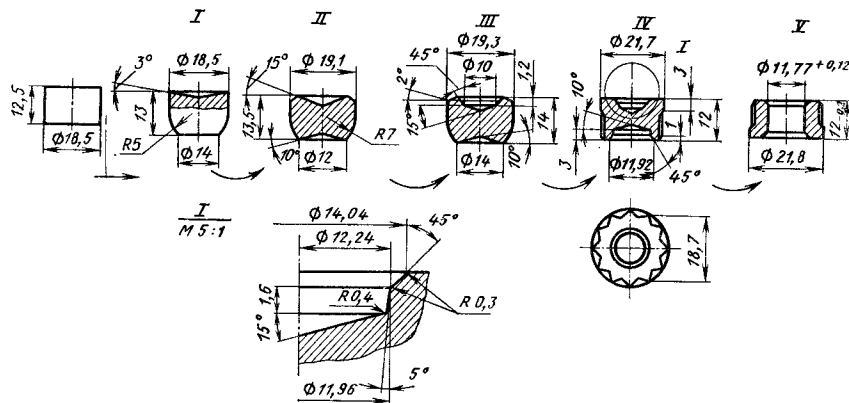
Технологический процесс штамповки заготовки гайки болта крепления крышки шатуна на пятипозиционном автомате
